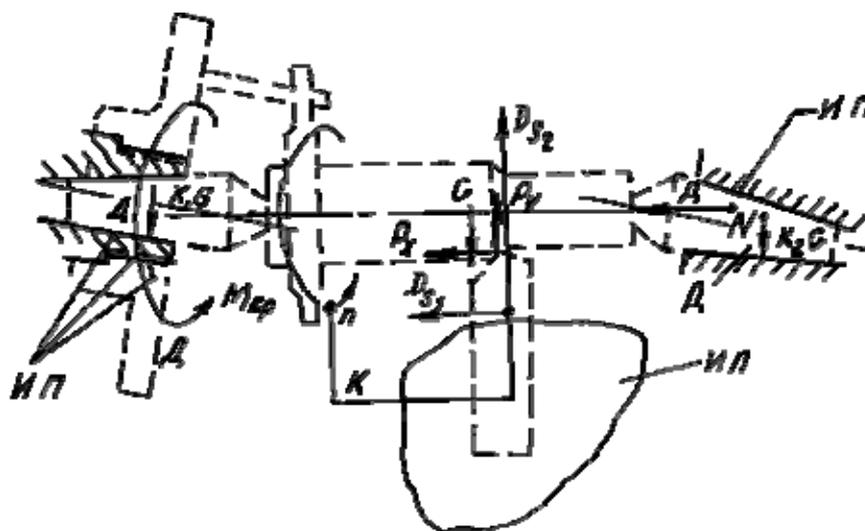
Исполнительные поверхности токарного станка и связи между ними
